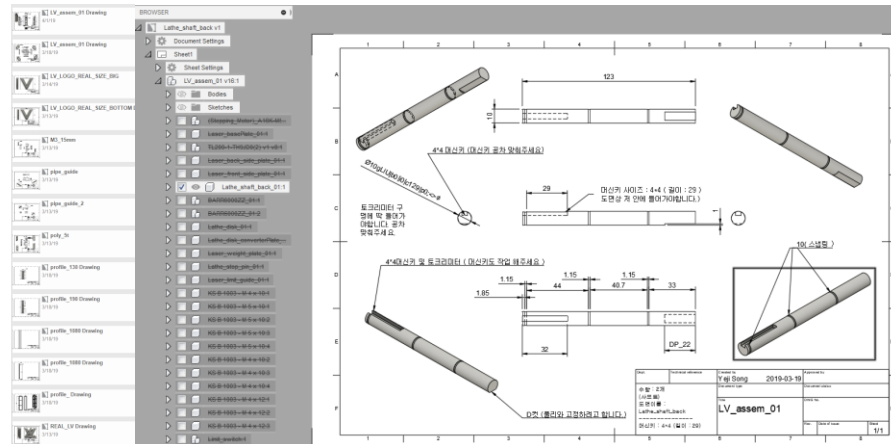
(Fusion 360 Drawing 기능을 활용하여 제조 도면 작성 예시. <위의 도면은 선반 작업 도면>)
